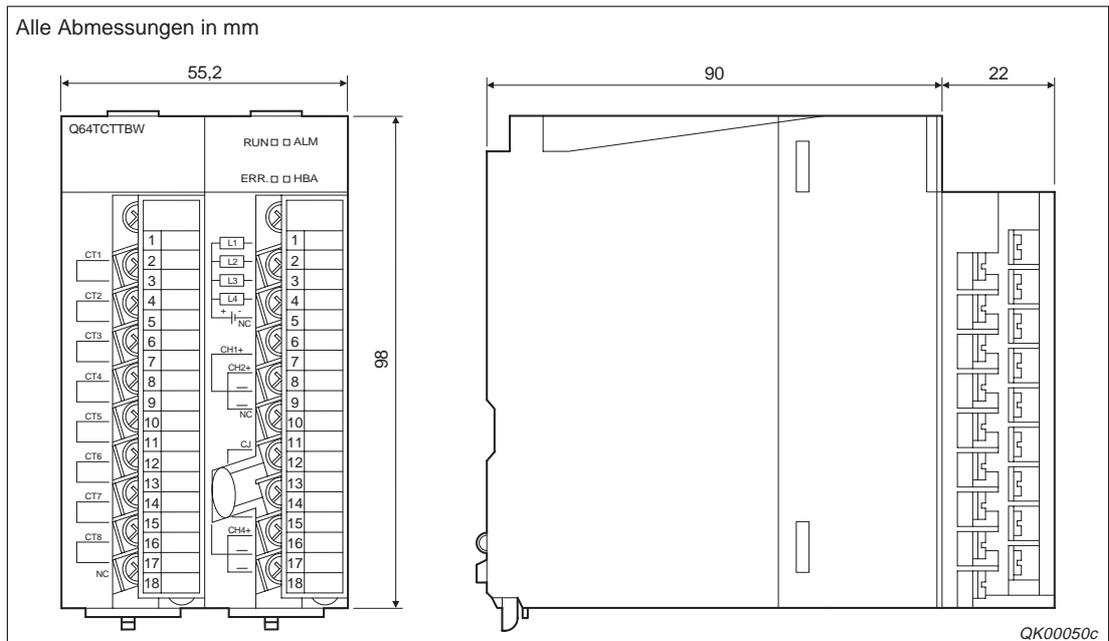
Abmessungen der Module Q64TCTTBW, Q64TCRTBW
